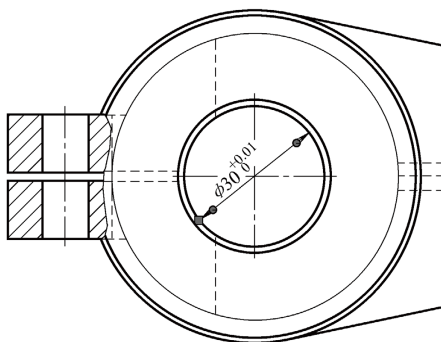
添加公差 / 精度后的尺寸标注
